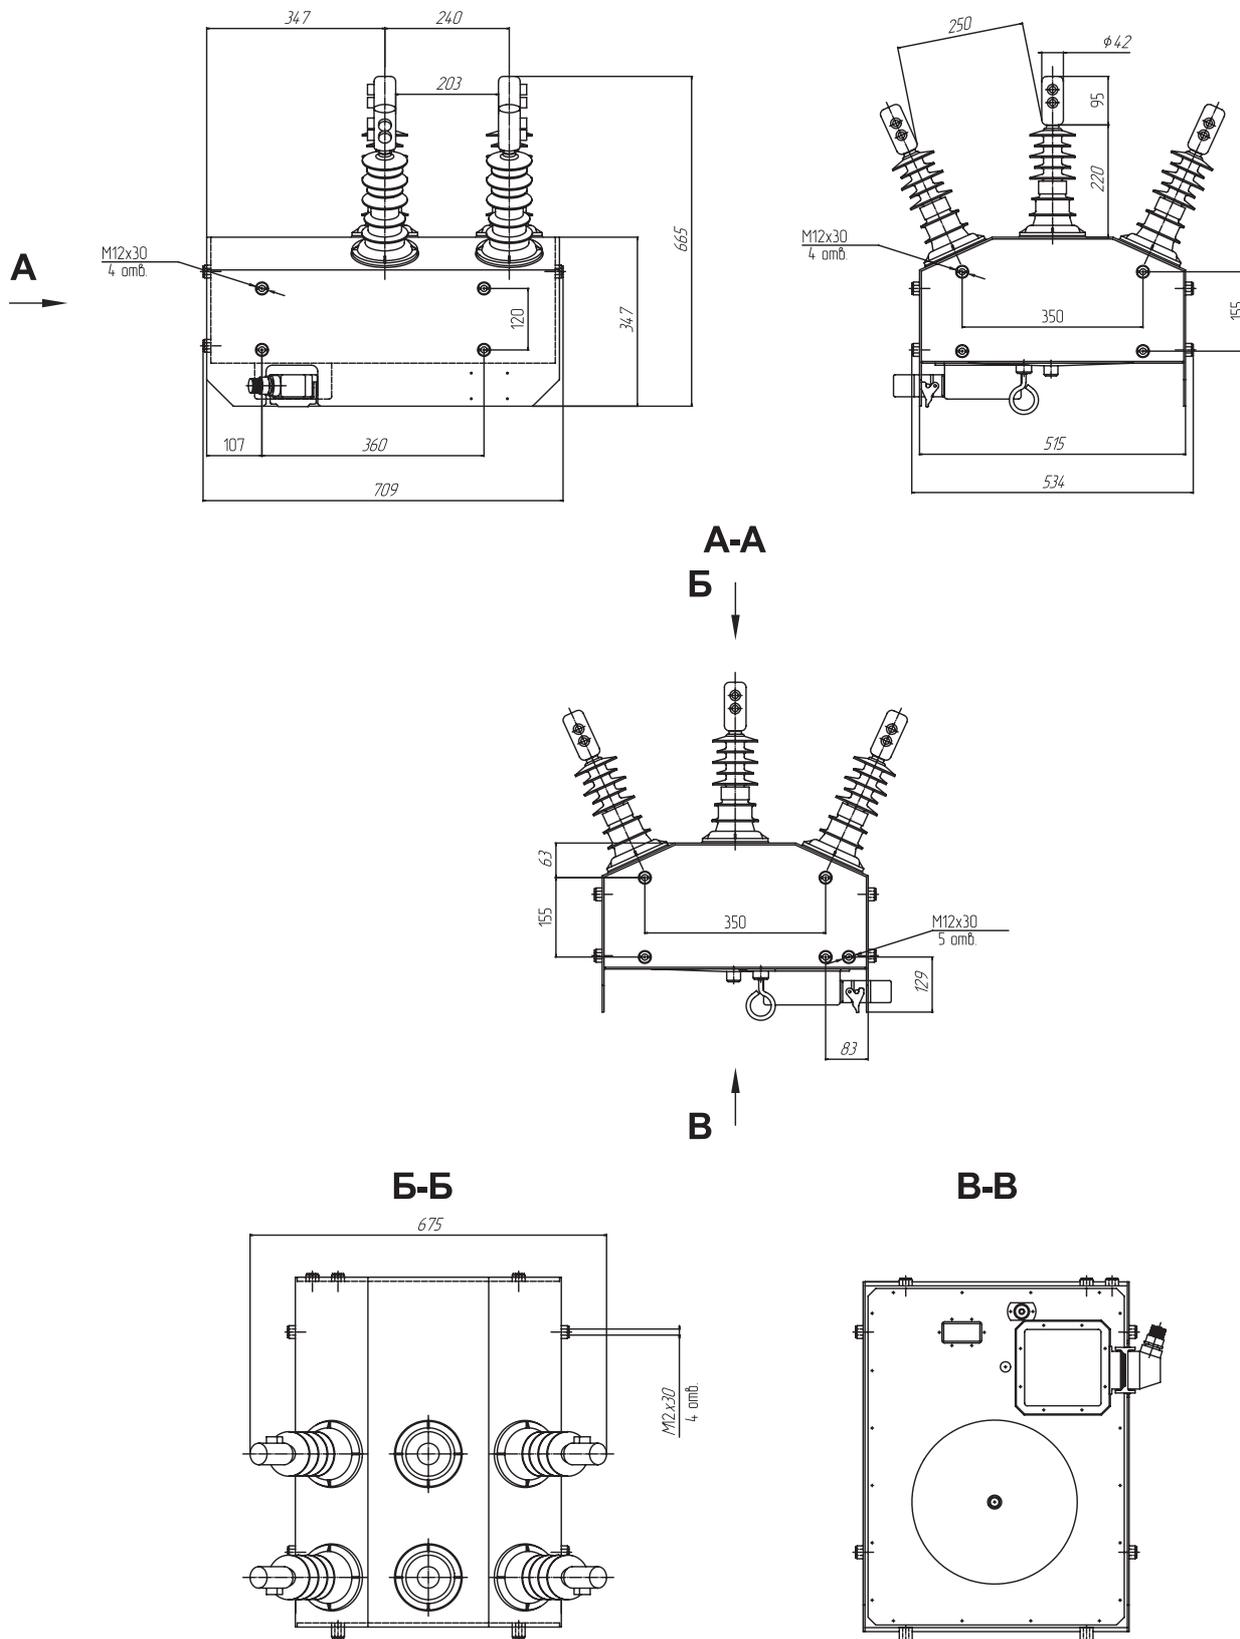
Габаритные и присоединительные размеры OSM/TEL
